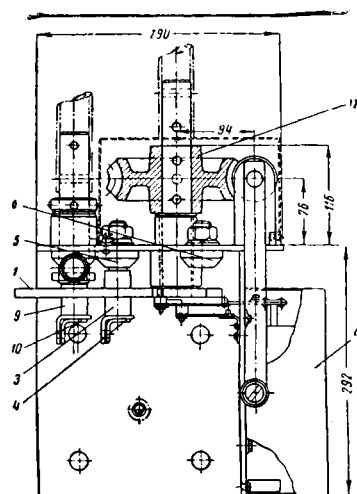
Привод рычажный типа ПРН-110: 1—корпус; 2—вал; 3—рычаг; 4—фиксатор; 5—втулка фиксатора; 6 и 7—упоры; 8—блок-контакты; 9—втулка вала
